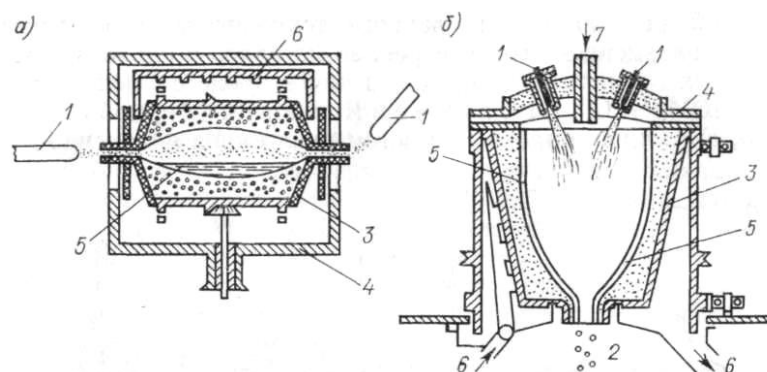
Схематичний вид обертових плазмових печей [58]: *а)* – з горизонтальною віссю; *б)* – з вертикальною віссю: 1 – електроди плазмотрона; 2 – готовий продукт; 3 – обертовий корпус печі; 4 – зовнішній
